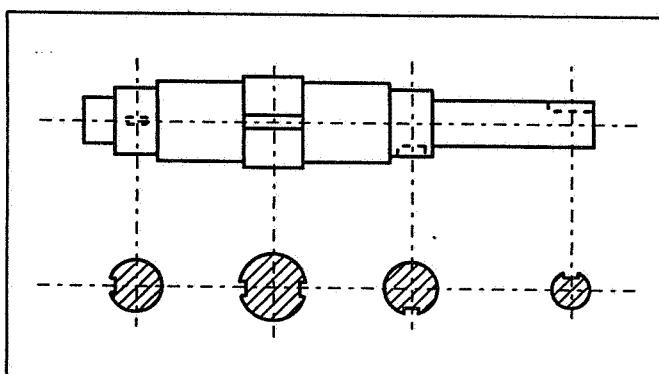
Sezioni successive su un albero poste sul prolungamento delle tracce dei piani di sezione; non occorre l'indicazione del piano di sezione.
